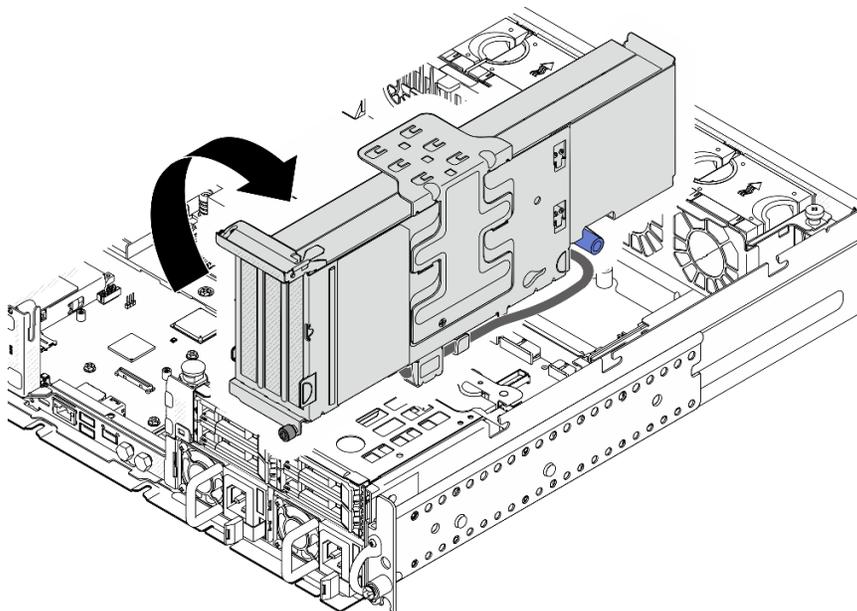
Colocar la expansión PCIe 2 a un lado del chasis
